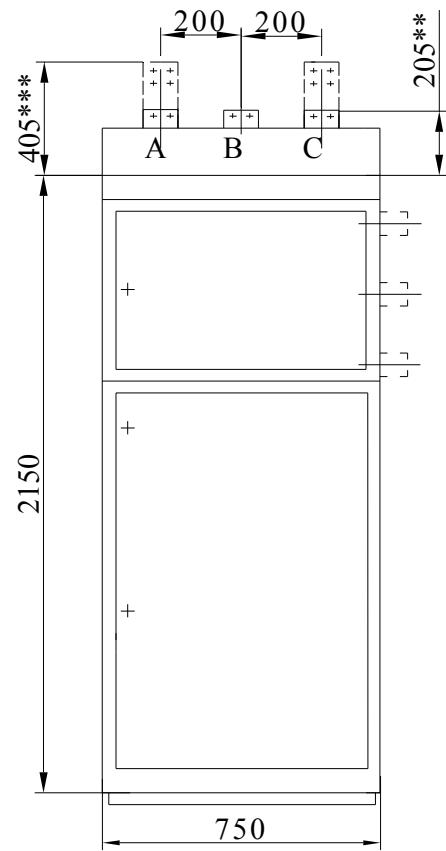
Габаритные, установочные и присоединительные размеры шкафов КРУ серии КМ-1ФМ шириной 750 mm
